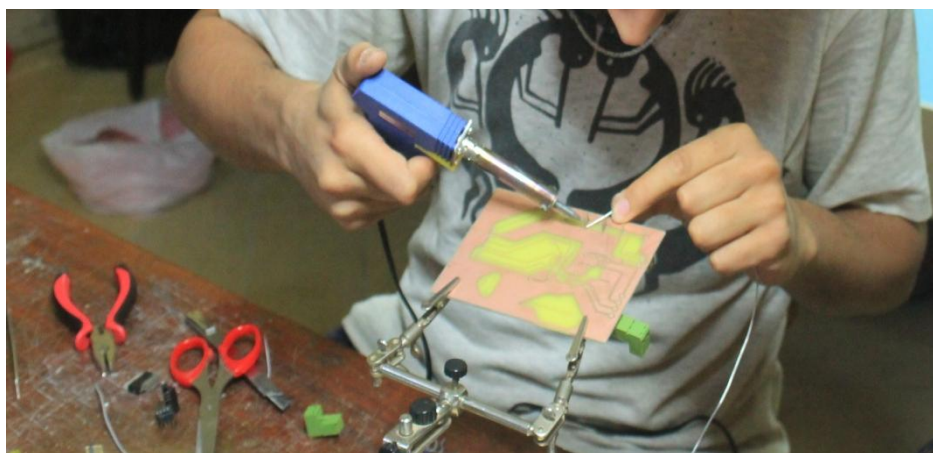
Soudure des composants sur la carte de puissance.
